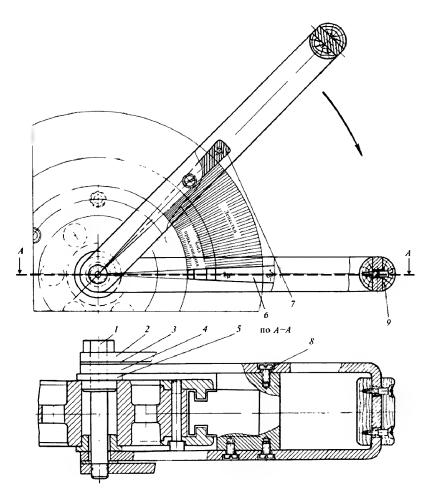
Приспособление для набора и приклеивания лепестков вручную: I- болт; 2- вилка наружная; 3- шайба; 4- вилка внутренняя; 5- втулка;  $6,\ 7-$  щеки; 8- винт; 9- накладка
